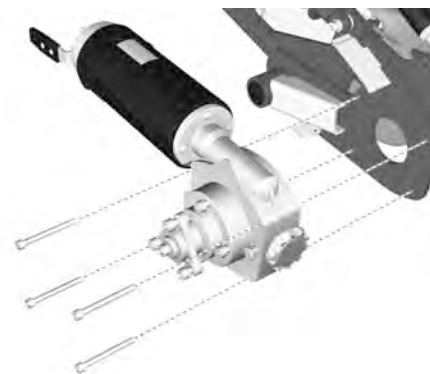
Anbringen oder Ausbauen des Antriebsmotors.
